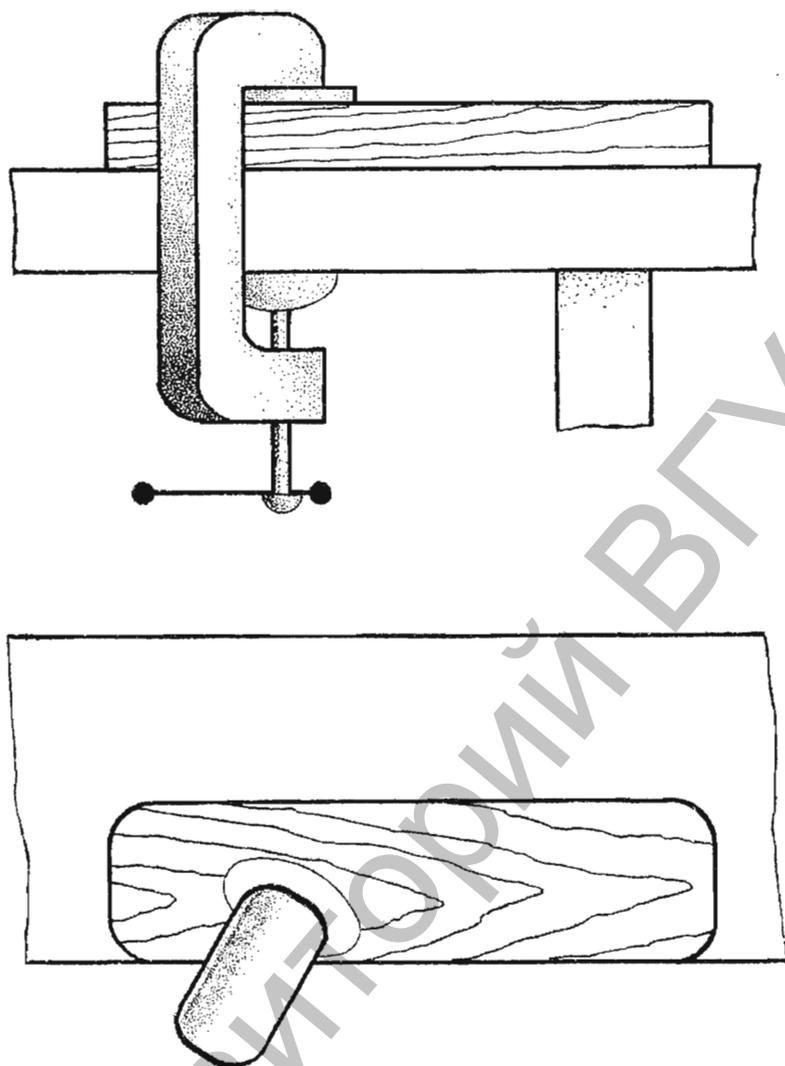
Крепление заготовки для резьбы при помощи струбцины.
